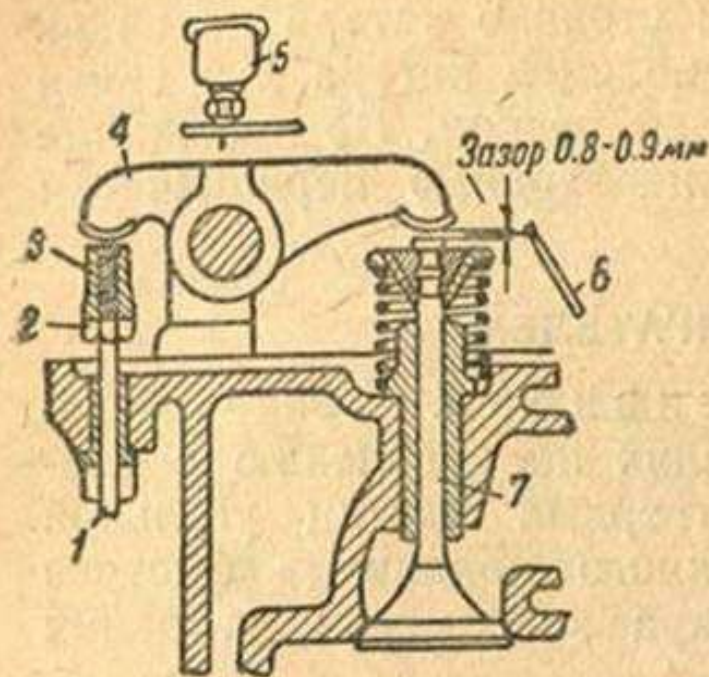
Регулировка зазора между стержнем клапана и коромыслом путем изменения положения регулировочной гайки (двигатель ЧТЗ-60):
